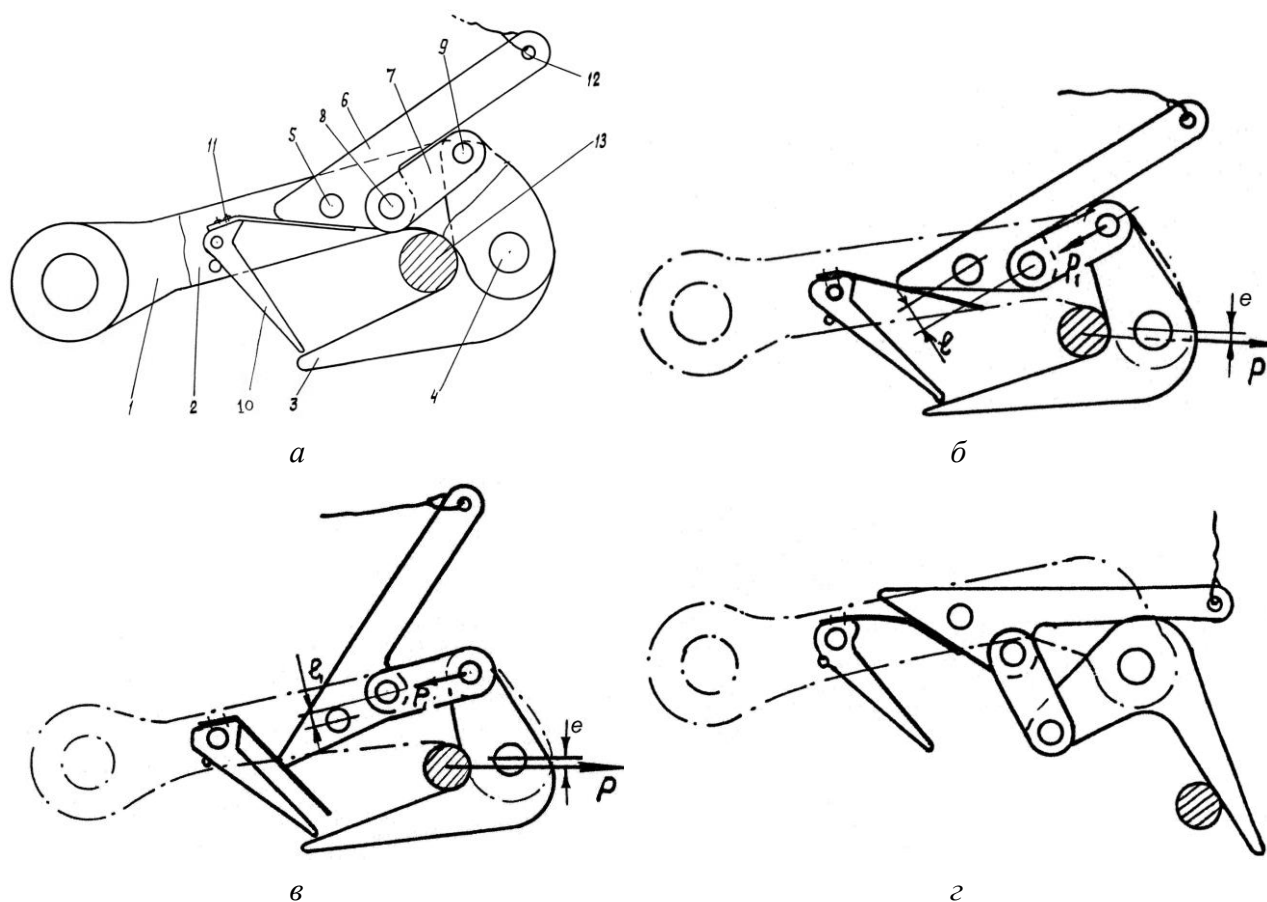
Такелажный замок: а – закрытый такелажный замок, местный размер на виде сбоку; б – расположение деталей закрытого замка; в – расположение деталей в начальный момент открытия замка при приложении нагрузки к рычагу; з – расположение деталей открытого замка.
